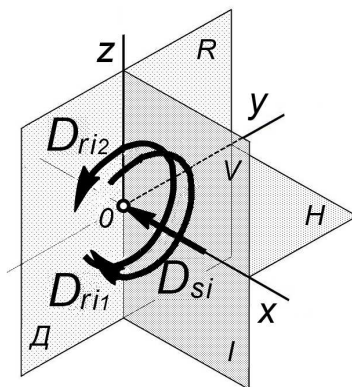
Принципова кінематична схема механічного оброблення отвору
